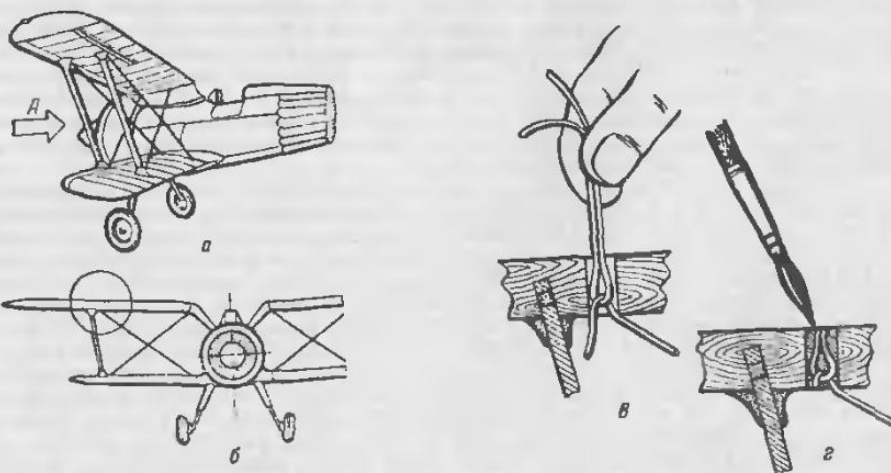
Установка расчалок: а - общий вид; б - вид спереди; в, г - заделка концов расчалок
